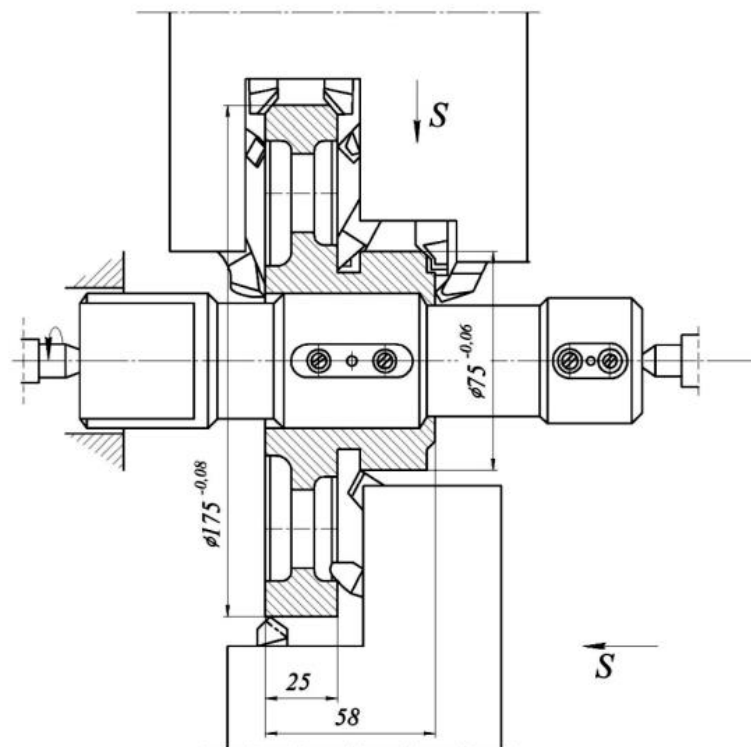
Схема налагодження для оброблення блоку зубчастих коліс на одношпиндельному багато різцевому токарному напівавтоматі
